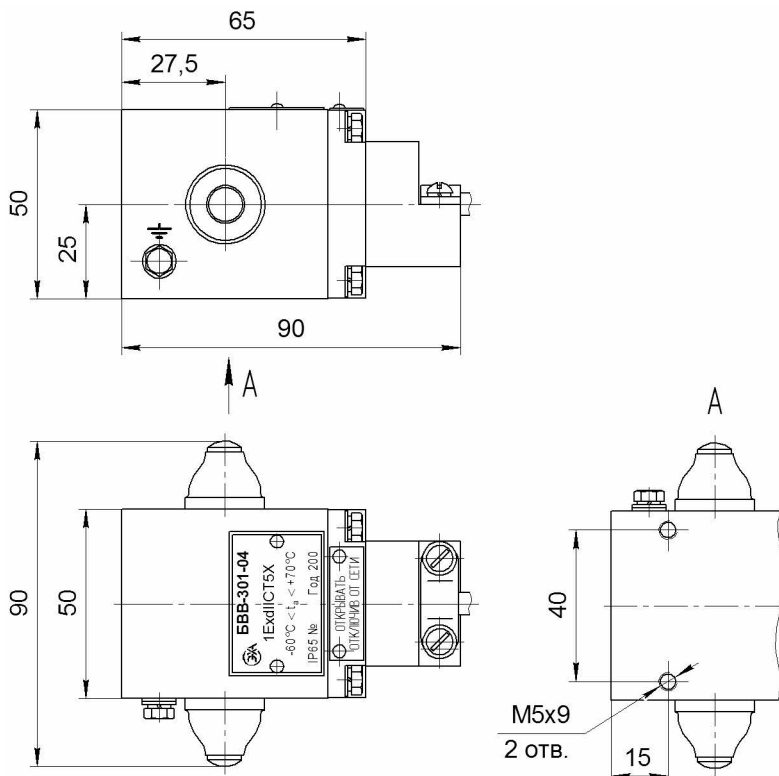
Габаритные и установочные размеры блока выключателей БВВ-301-04
